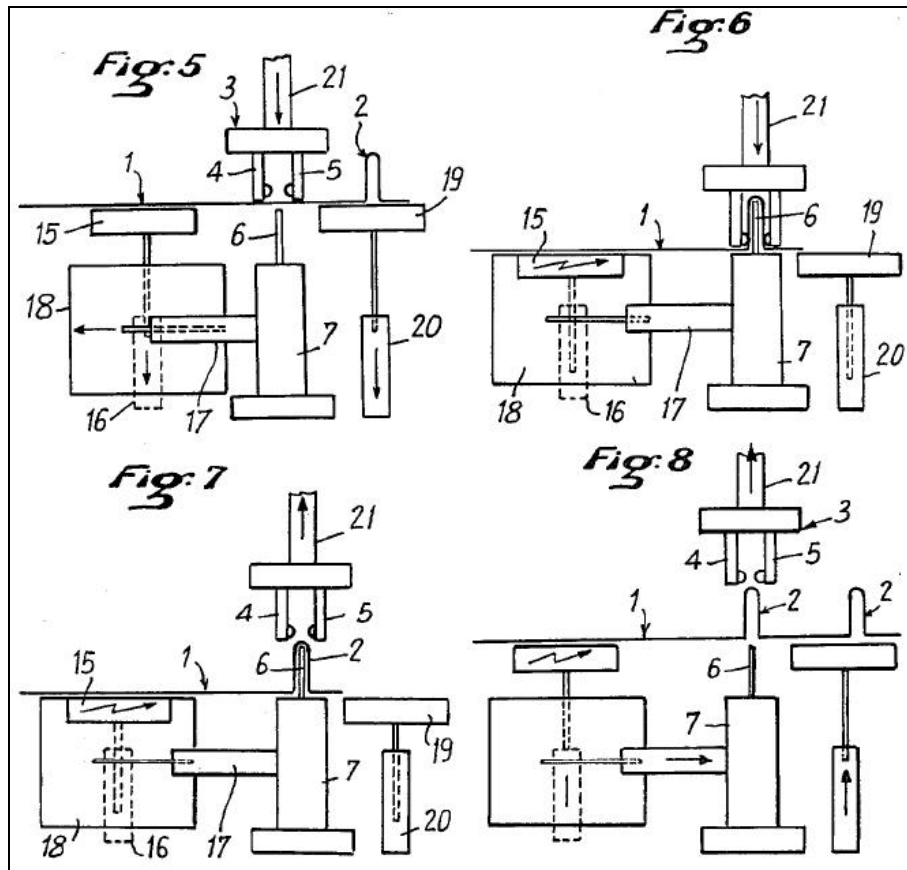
Esquema de una Maquina plegadora y soldadora de aristas [8]
